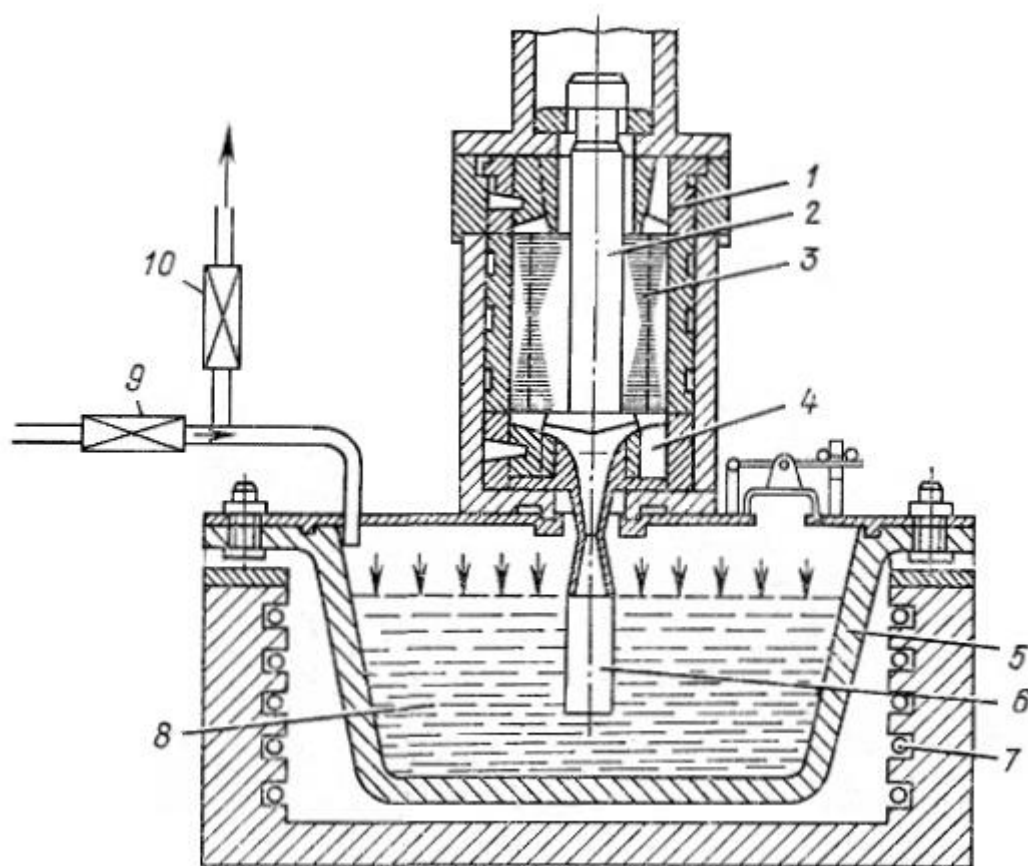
Схема заливки роторов под низким давлением: 2-подвижная часть формы; 3-пакет ротора; 4-неподвижная часть формы; 5-тигель; 6-металлопровод; 7-печь; 8-воздухопровод
